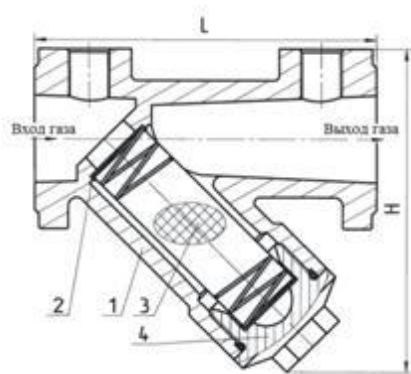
Фильтр сетчатый типа ФС: 1 - корпус; 2 - кассета; 3 - сетка; 5 - крышка
